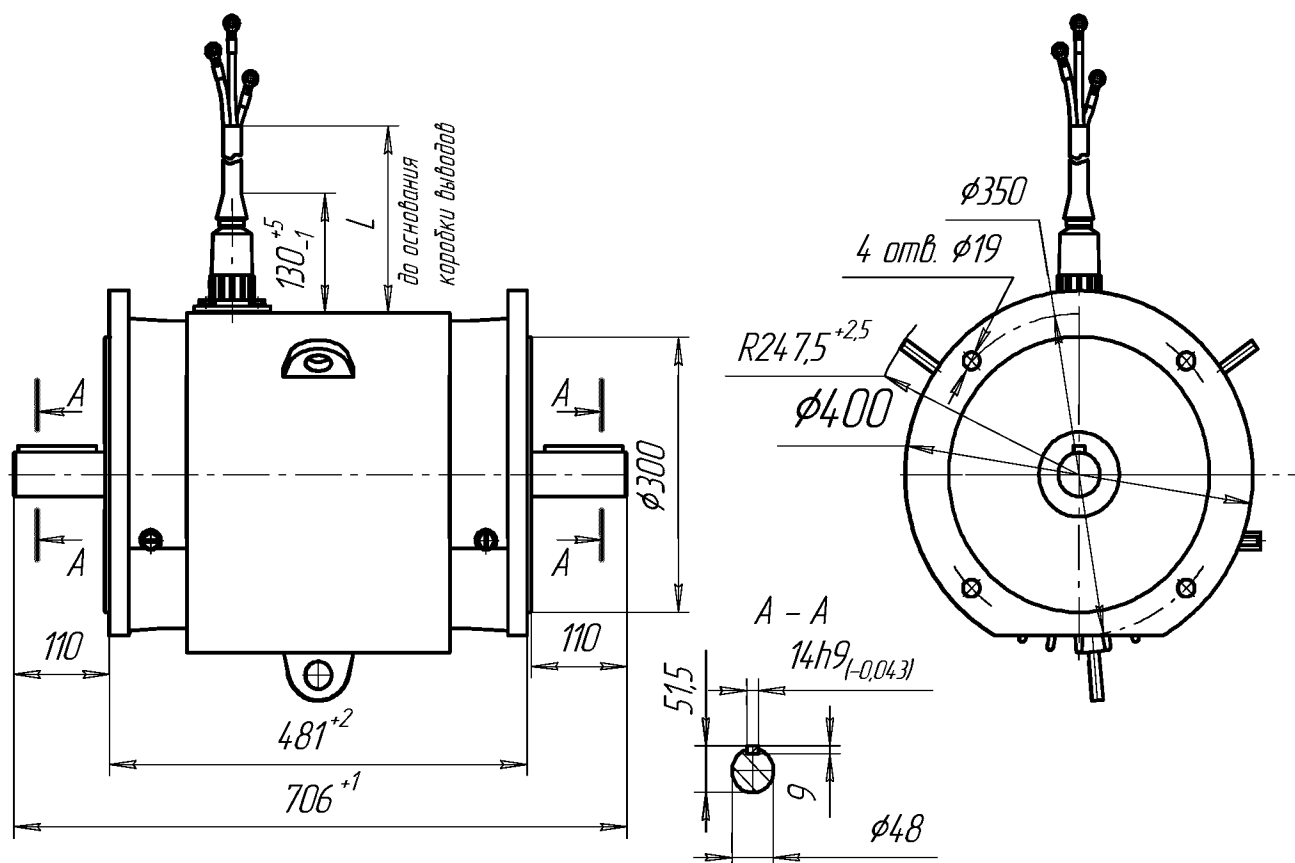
Габаритные, установочные и присоединительные размеры электродвигателя рДМ180 М2
